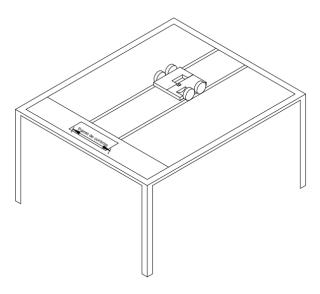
Modelo simplificado da estrutura do guindaste no AutoCAD
